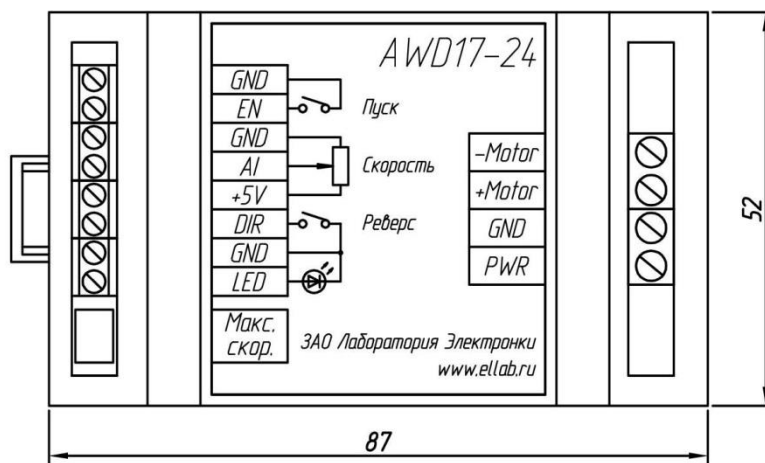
Габаритные размеры блока управления в корпусе на DIN рейку
